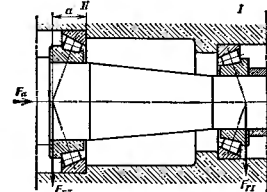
Схема установки конических роликоподшипников в ступице колеса
